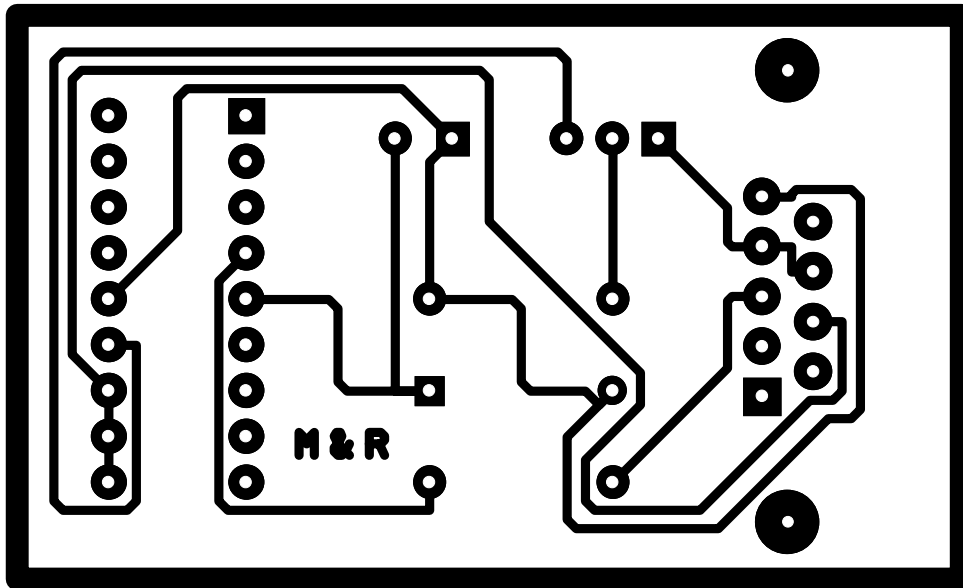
Cara de soldadura de la placa PCB del programador JDM. Si utilizamos un cable null modem (DB9(hembra)-DB9(hembra)) habrá que comprar un conector DB9(macho) para la PCB y habrá que revisar la cara de soldadura.
